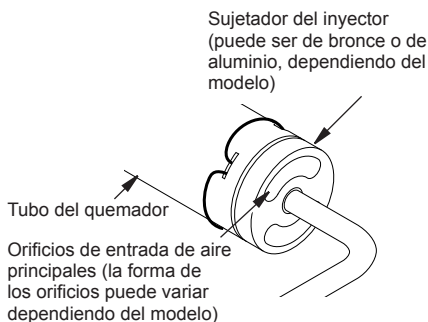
Sujetador del inyector en el tubo de salida del quemador
